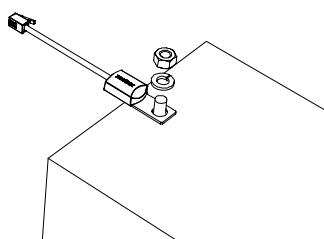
Instalación del sensor BTS en un terminal de la batería
